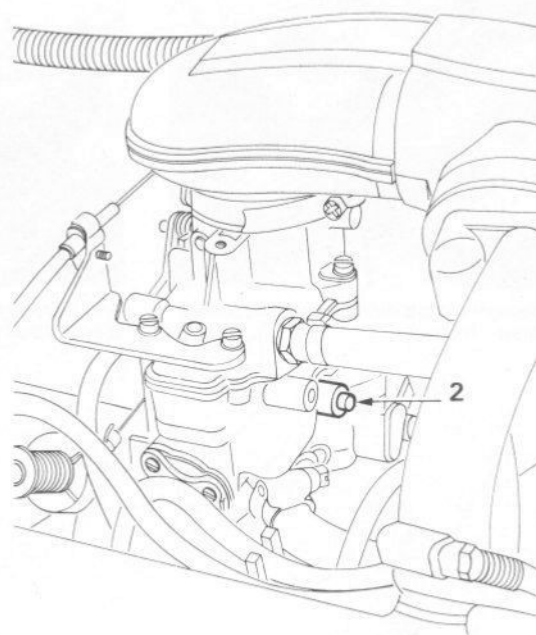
Position de la vis de richesse (2) - carburateur Weber 32 IBSH (Sec 8)
